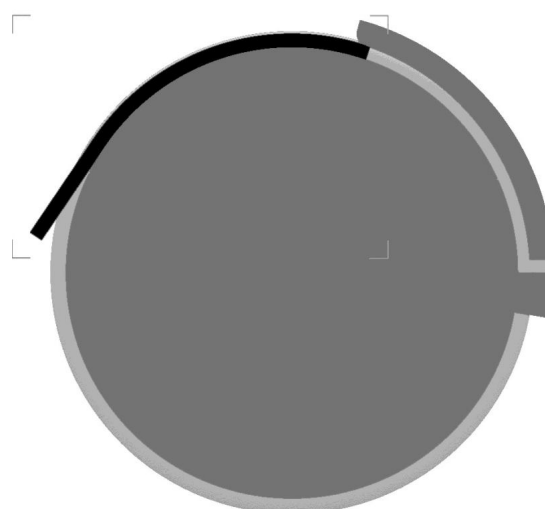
Эскиз первоначального положения заготовки в канале прессования
